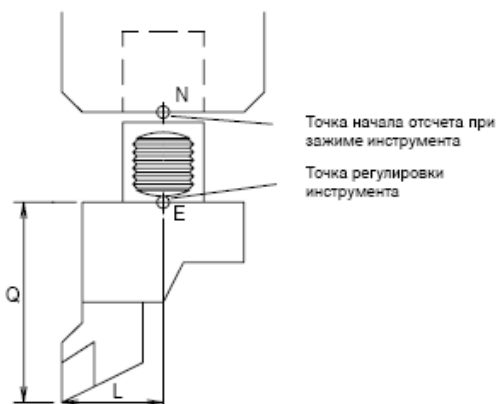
Точка регулировки инструмента и точка начала отсчета при зажиме инструмента
